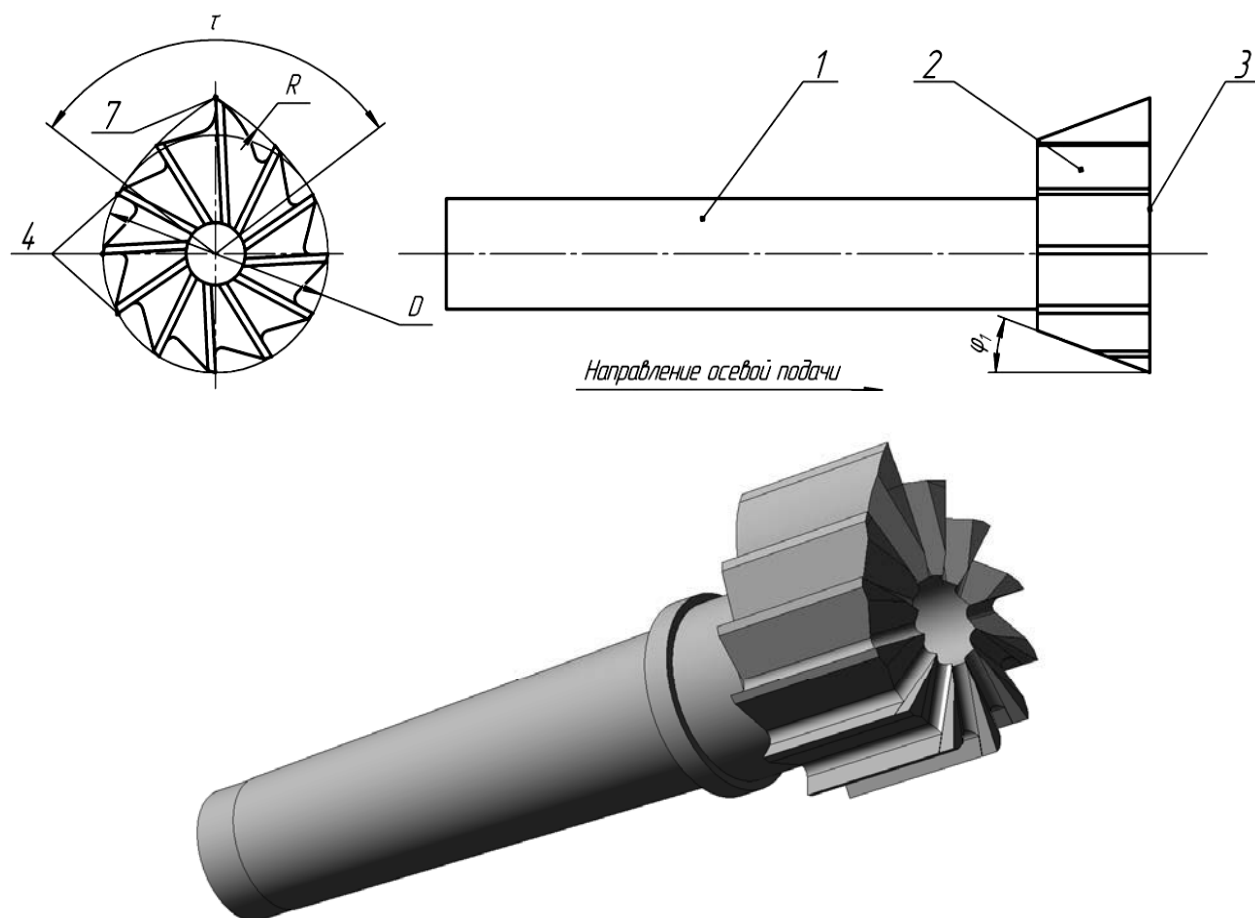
Инструмент для формирования контура статора роторно-поршневого двигателя
